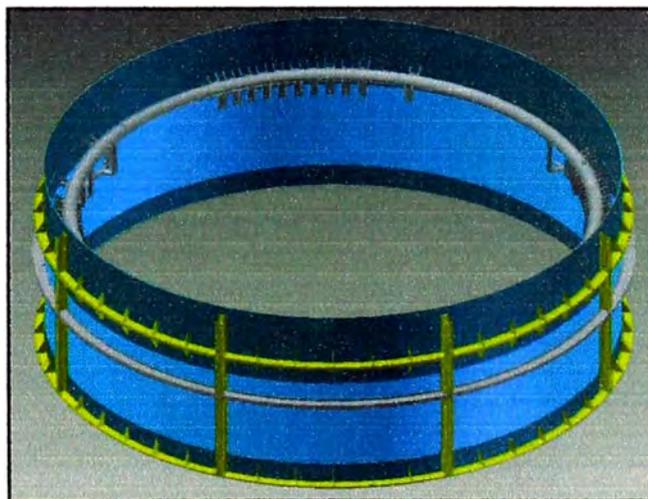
Montaje de loa Anillos 10-11 en piso
